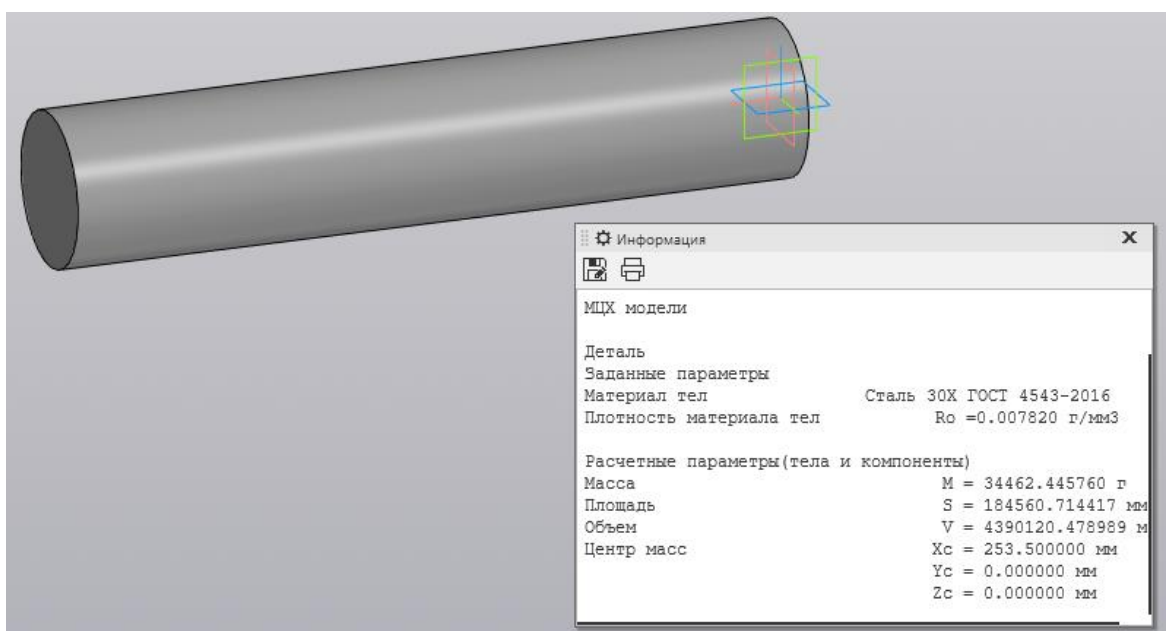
3D модель заготовки виготовленої з прокату
